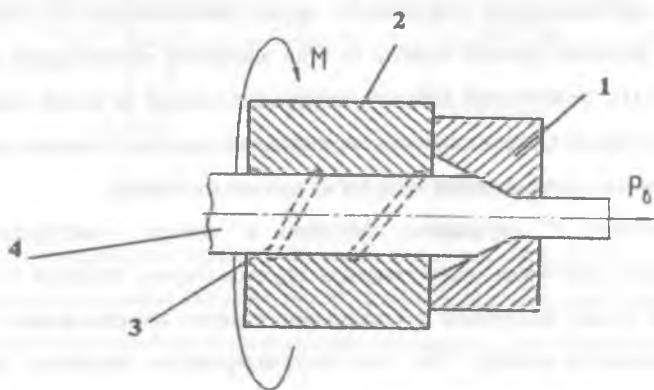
Устройство для совмещения волочения с кручением заготовки перед входом в волоку
